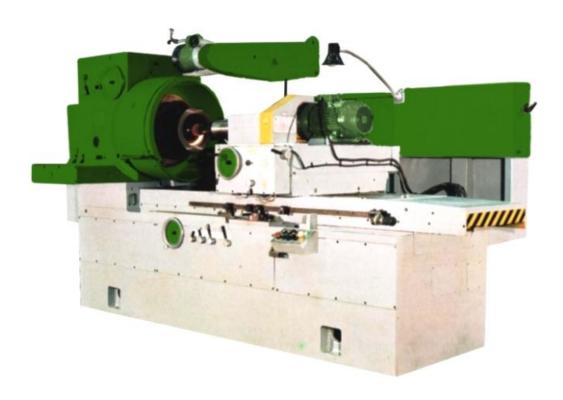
внутришлифовальный станок универсальный 3К229А
